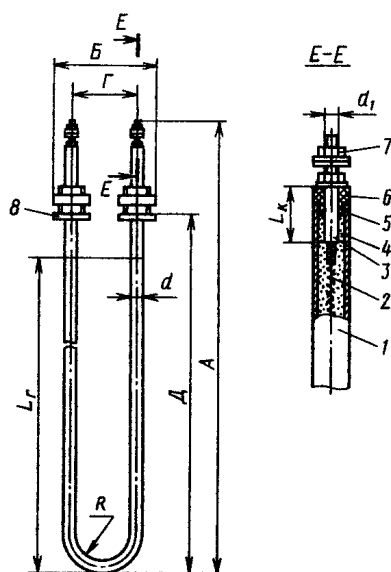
Устройство трубчатого электронагревателя: 1 — тонкостенная металлическая оболочка; 2 — спираль; 3 — контактный стержень; 4 — наполнитель; 6 — герметик; в — изолятор; 7 — гайка; 8 — крепежное устройство
